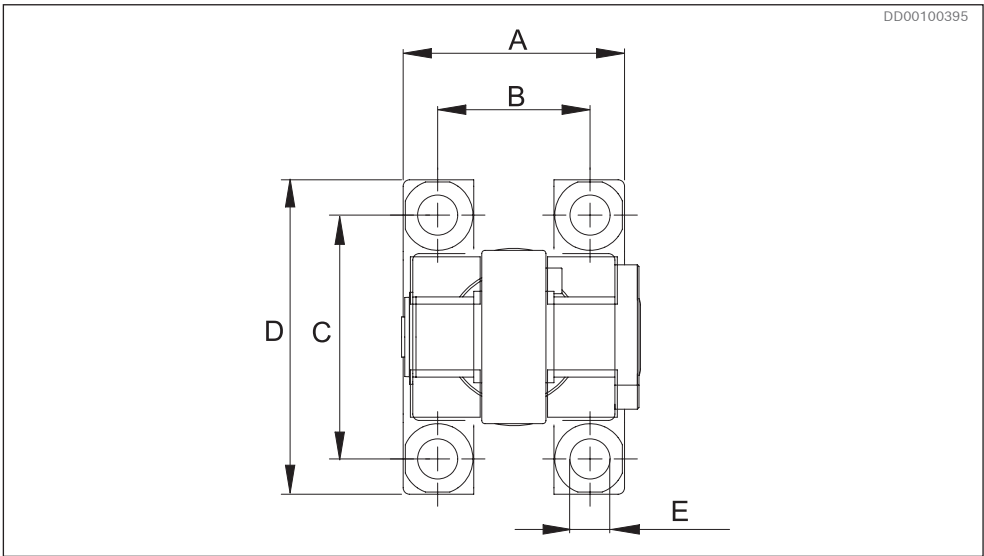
Bohrbild für Montage von Gelenkverbindung und Hydraulikzylinder für DTCB
